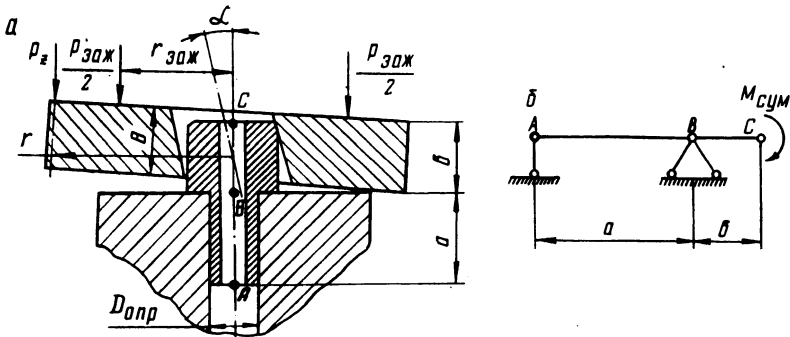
Схема установки цилиндрического зубчатого колеса при зубофрезеровании:
